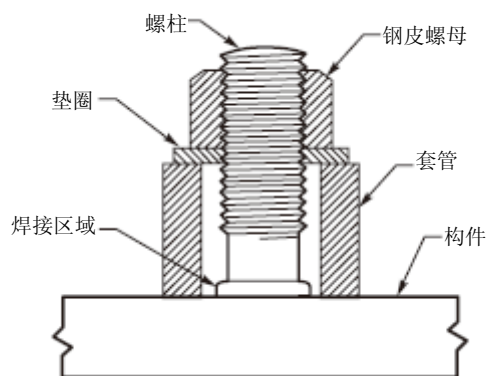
用于螺柱焊缝的典型拉伸试验夹具
